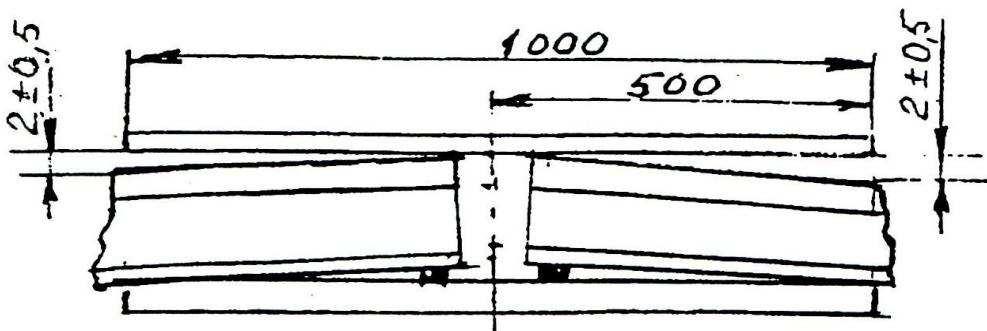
Схема измерения высоты установки концов рельсов перед сваркой
